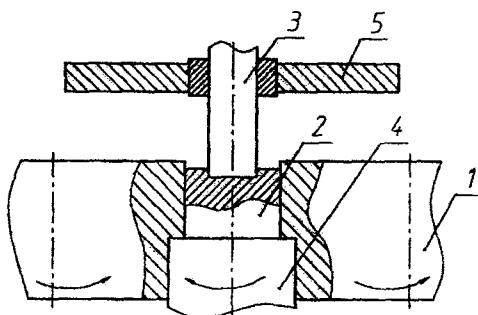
Валковая штамповка: 1 – валки; 2 – обрабатываемая заготовка; 3 – пуансон; 4 – контрпуансон, задающий вращение; 5 – съемник
